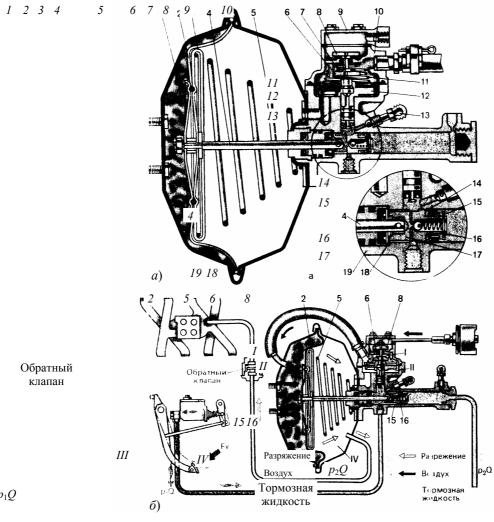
Гидровакуумный усилитель тормозного привода автомобиля ГАЗ-66:
